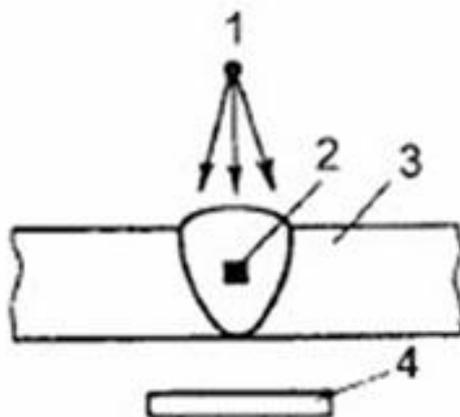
Схема просвечивания сварного соединения
